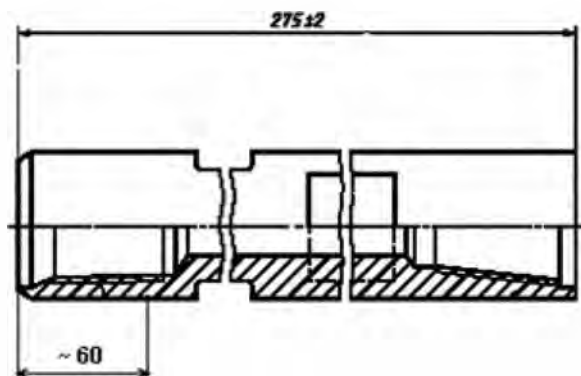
Схема излома муфты со стороны замковой резьбы
